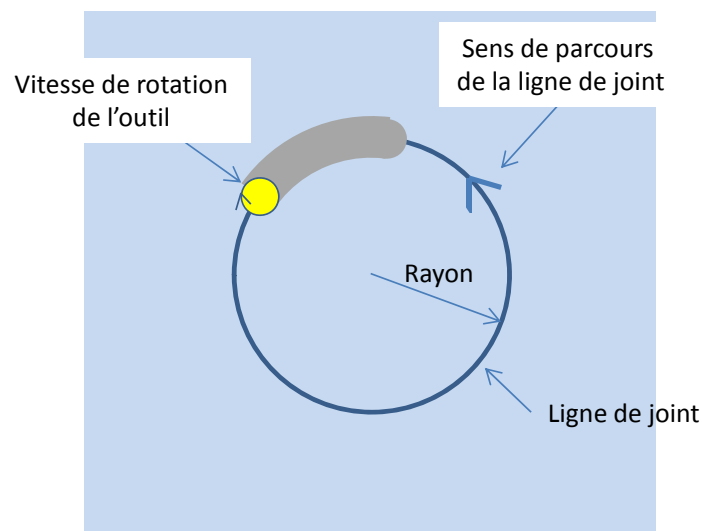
Schéma d'une soudure circulaire paramétrée
